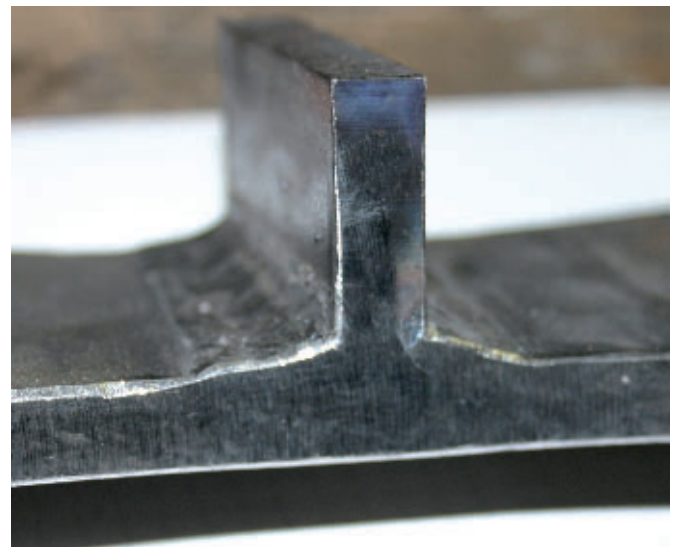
Ansicht auf die Schweißnähte nach der Sanierung
